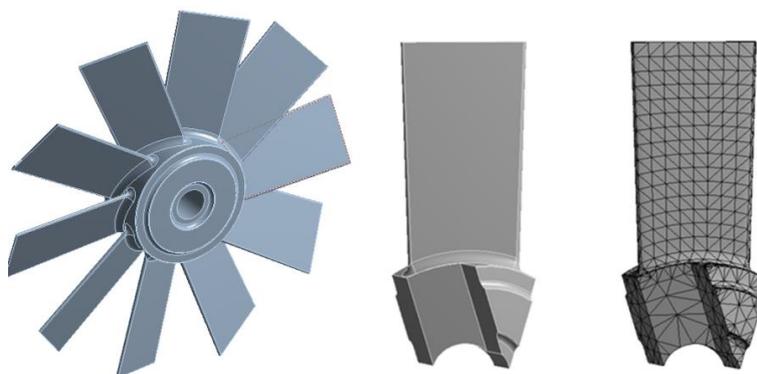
Общий вид и КЭМ академического рабочего колеса
